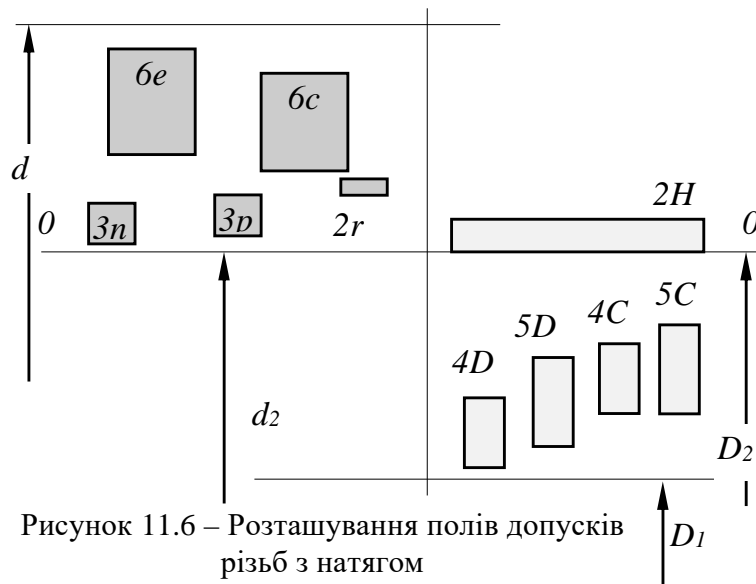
Розташування полів допусків різьб з натягом
